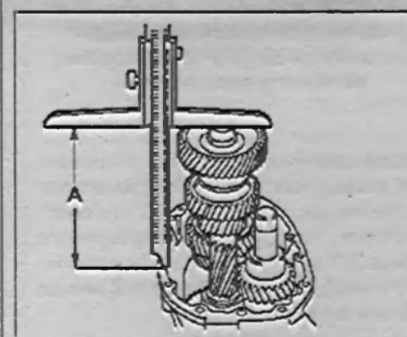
Измерьте расстояние «А» от промежуточного вала до уплотнительной поверхности передней части корпуса коробки передач.
